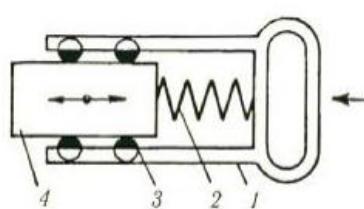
Схема віброізольованого держака: 1 – держак; 2 – пружний елемент; 3 – підшипник; 4 - корпус
